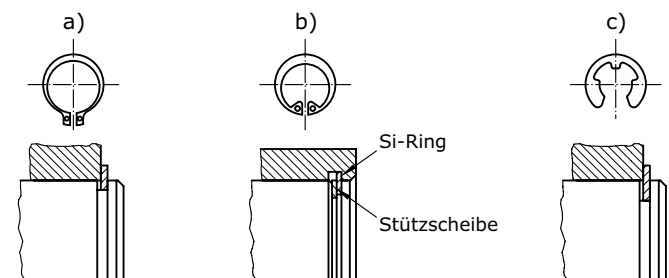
nvZ) Formschlüssige axiale Sicherungselemente a) axial montierbar aussen; b) axial montierbar innen; c) radial montierbar aussen
